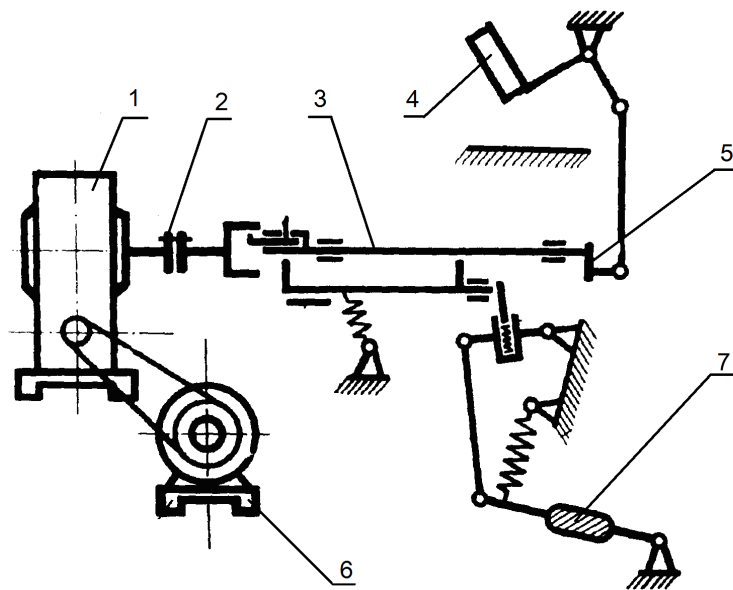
Кінематична схема установки ножового ковзного різання
